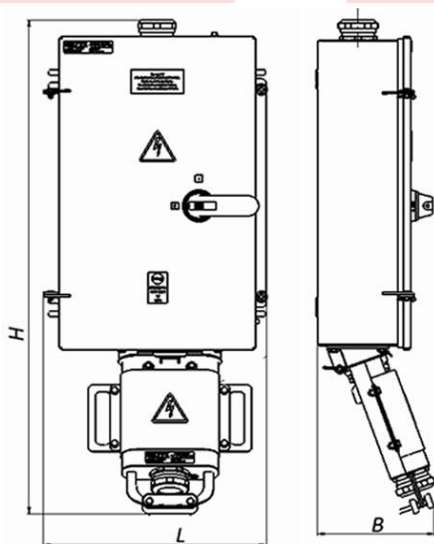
Общий вид и габаритные размеры ВРН-Ш/Р(Twin) 630 А без соединителя
